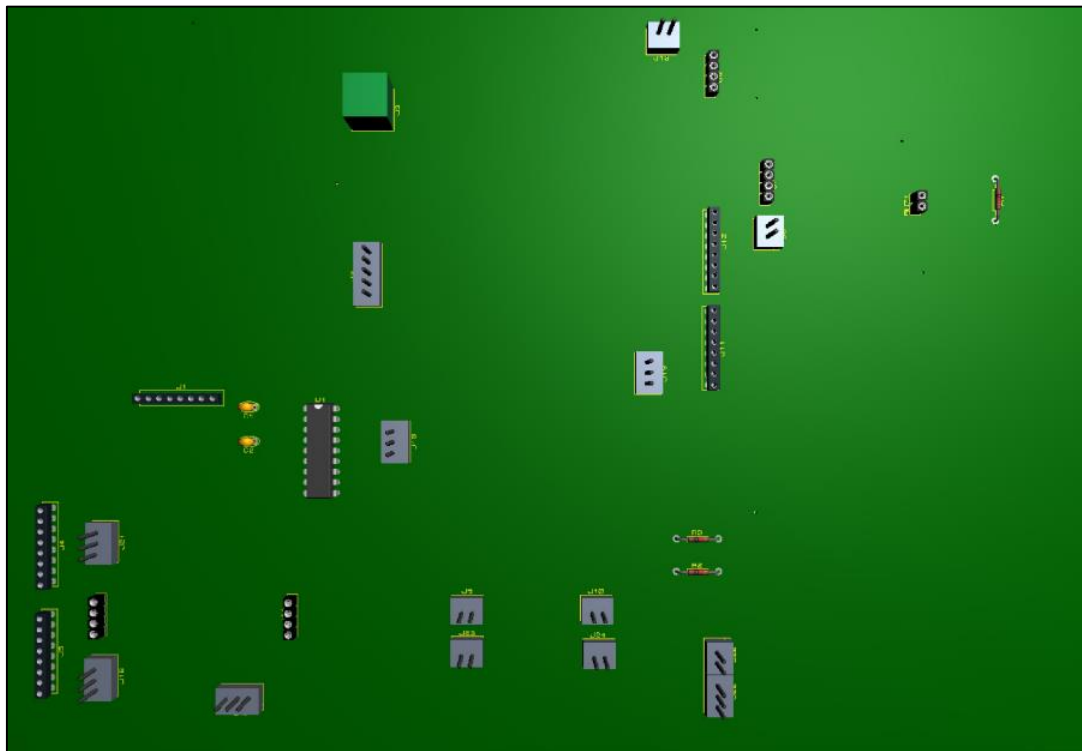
Diseño del módulo en Proteus para la PCB 3D
